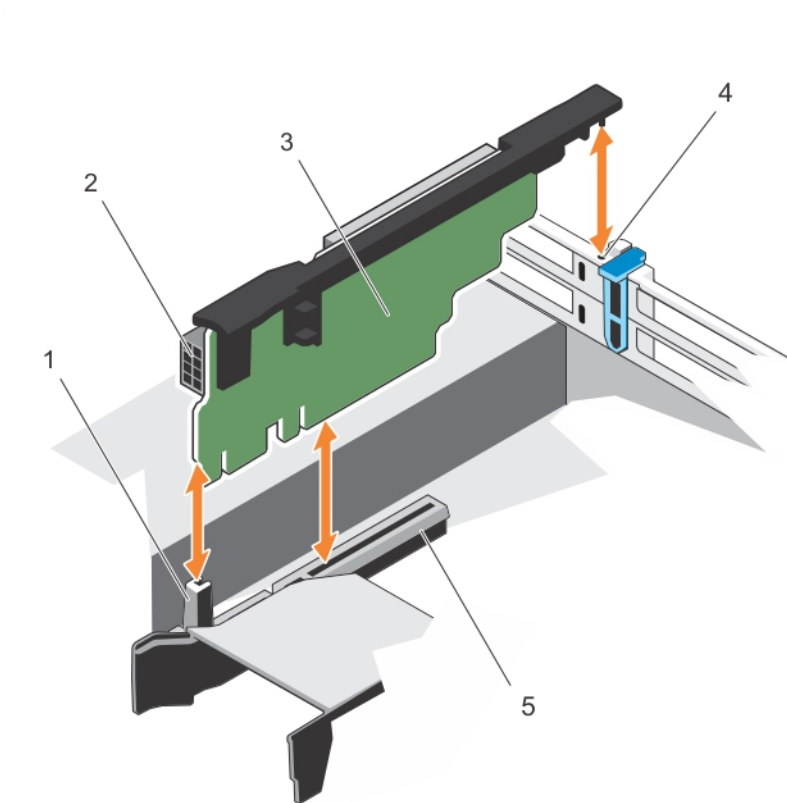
Remover e instalar a raiser da placa de expansão 2
